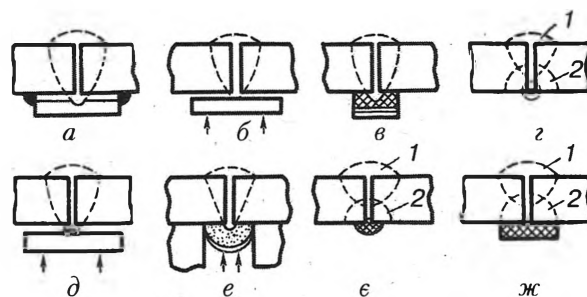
Схеми утримування зварювальної ванни і шлаку та формування зворотного валика при зварюванні під флюсом:
